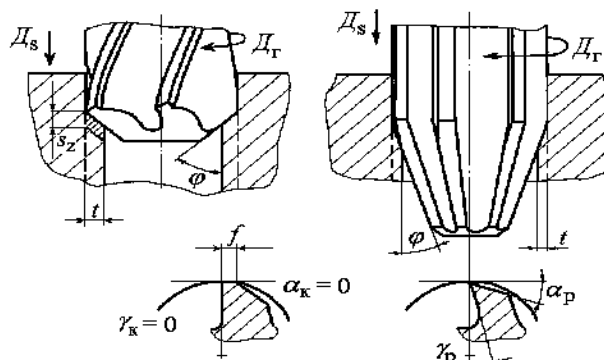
Элементы резания: а – при зенкеровании, б – развертывании; в – профиль режущей частей зуба развертки; г – профиль калибрующей частей зуба развертки.
